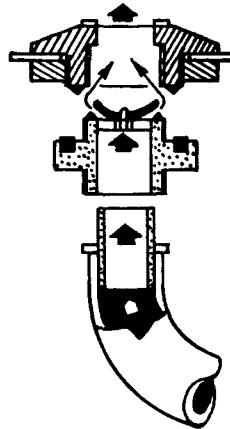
Схема соединения вентиля с эластичным тарельчатым лепестковым клапаном и шлангом меха-насоса
